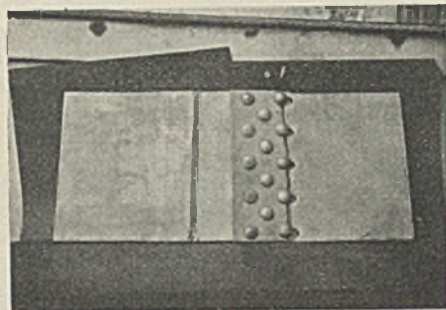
Zerreißversuche mit geschweißter und genietetem Blechnaht.
